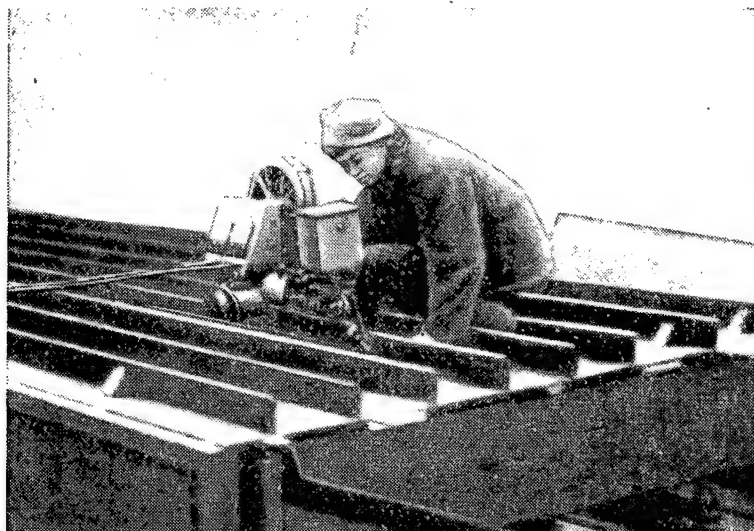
Электросварочный автомат типа АСУ-138 для сварки угловых швов
